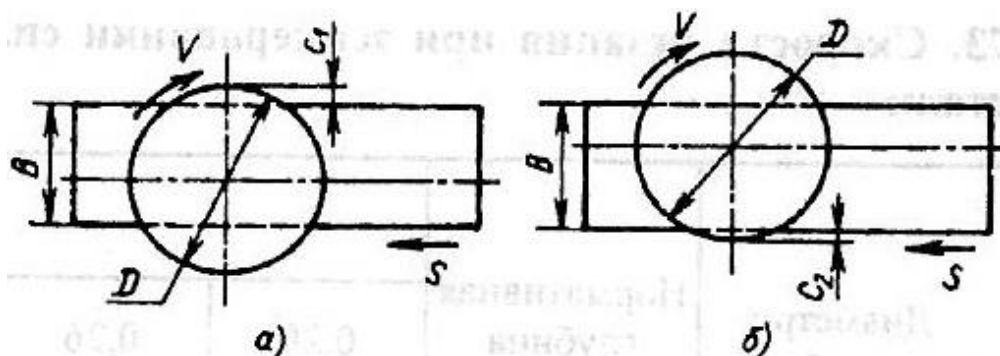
Расположение стальной заготовки при торцовом фрезеровании относительно фрезы: а – врезание зуба фрезы при $c_1 = (0,03 \dots 0,05)D$; б – выход зуба фрезы при $c_2 = 0$
